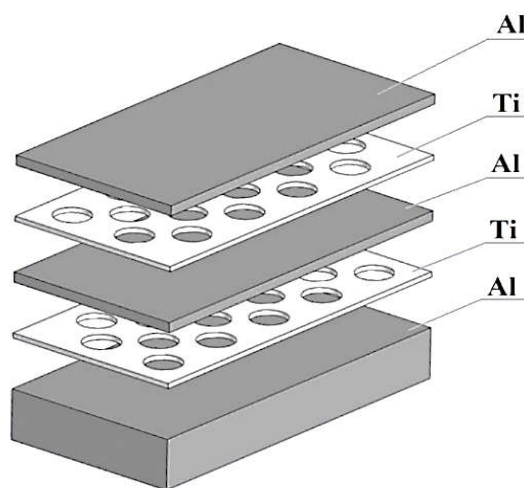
Схема сборки пакета композиционного материала перед сваркой взрывом
